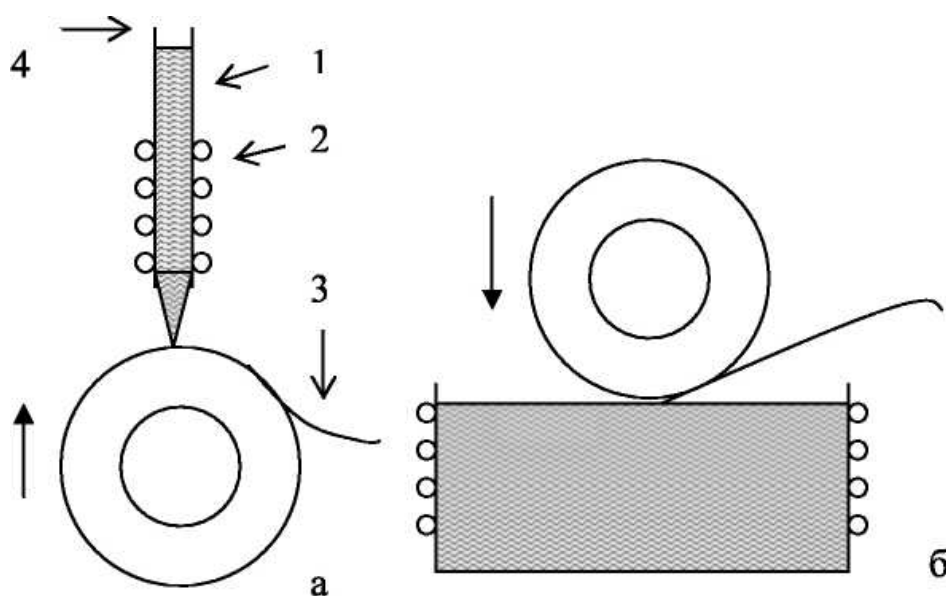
Схеми пристроїв для отримання АМС шляхом загартування з рідкого стану: 1 – розплав; 2 – нагрівальний пристрій; 3 – стрічка АМС; 4 – кварцова трубка [23]
